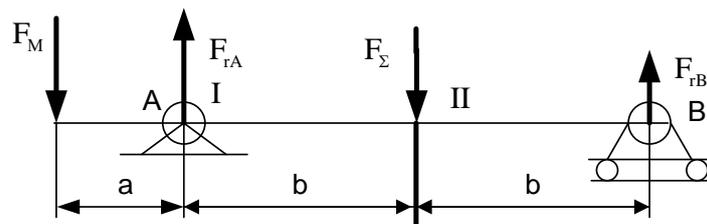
Расчётная схема для вала с одной тяговой звёздочкой
